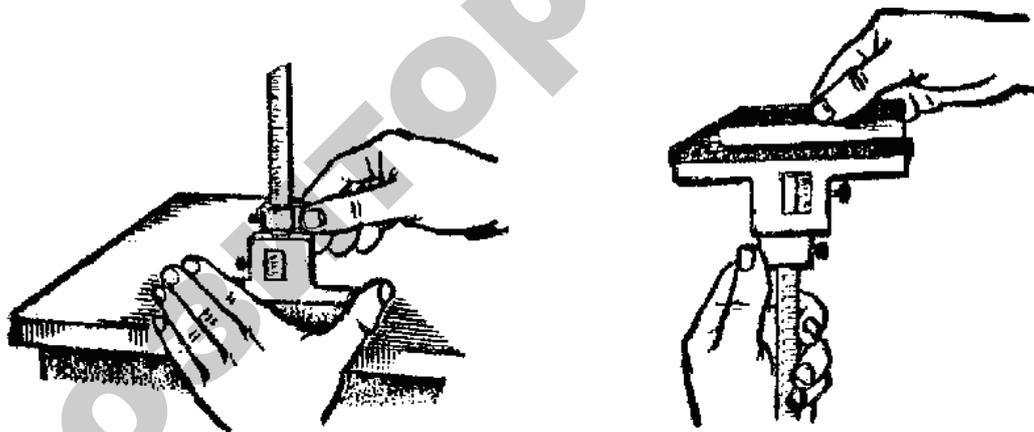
Проверка нулевого положения штангенглубиномера
